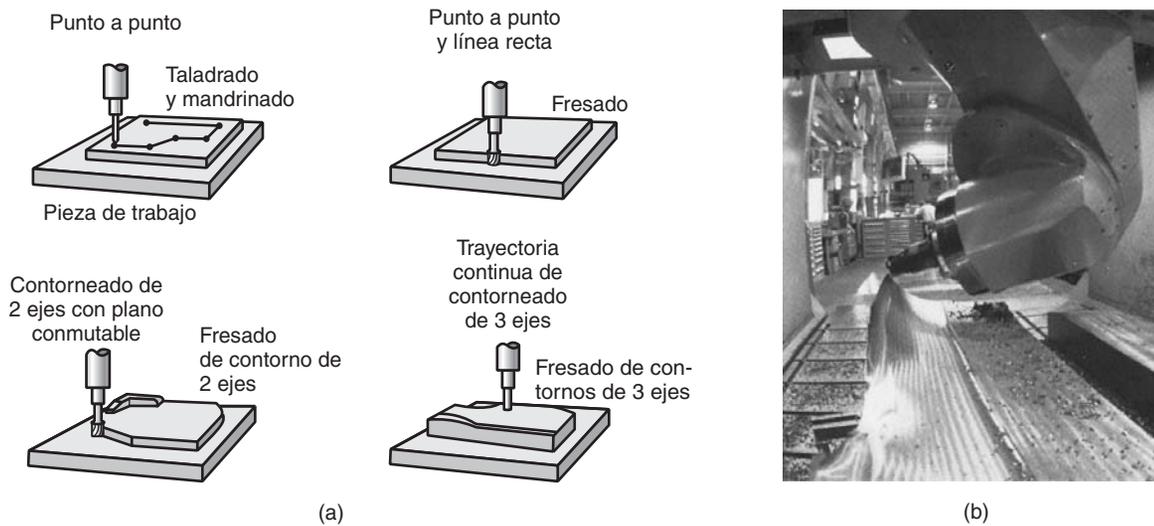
(a) Esquema de taladrado, mandrinado y fresado con diversas trayectorias. (b) Maquinado de una superficie esculpida en una máquina de control numérico de cinco ejes. Fuente: Cortesía de The Ingersoll Milling Machine Co.
